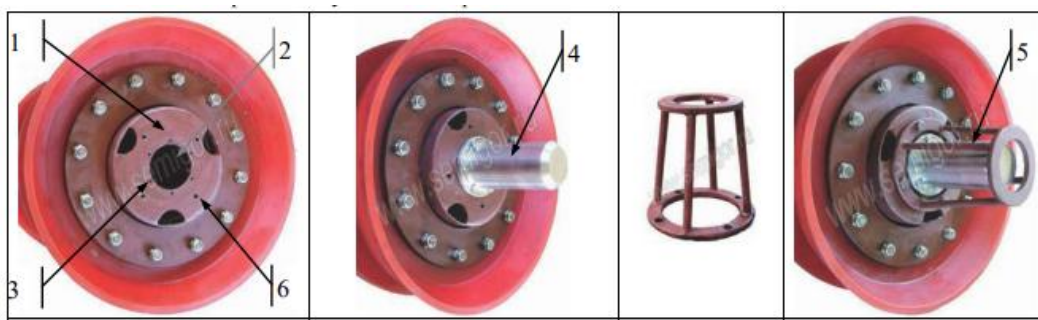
Установка передатчика на поршень. 1 – место для закрепления передатчика; 2 – посадочное отверстие; 3 –
